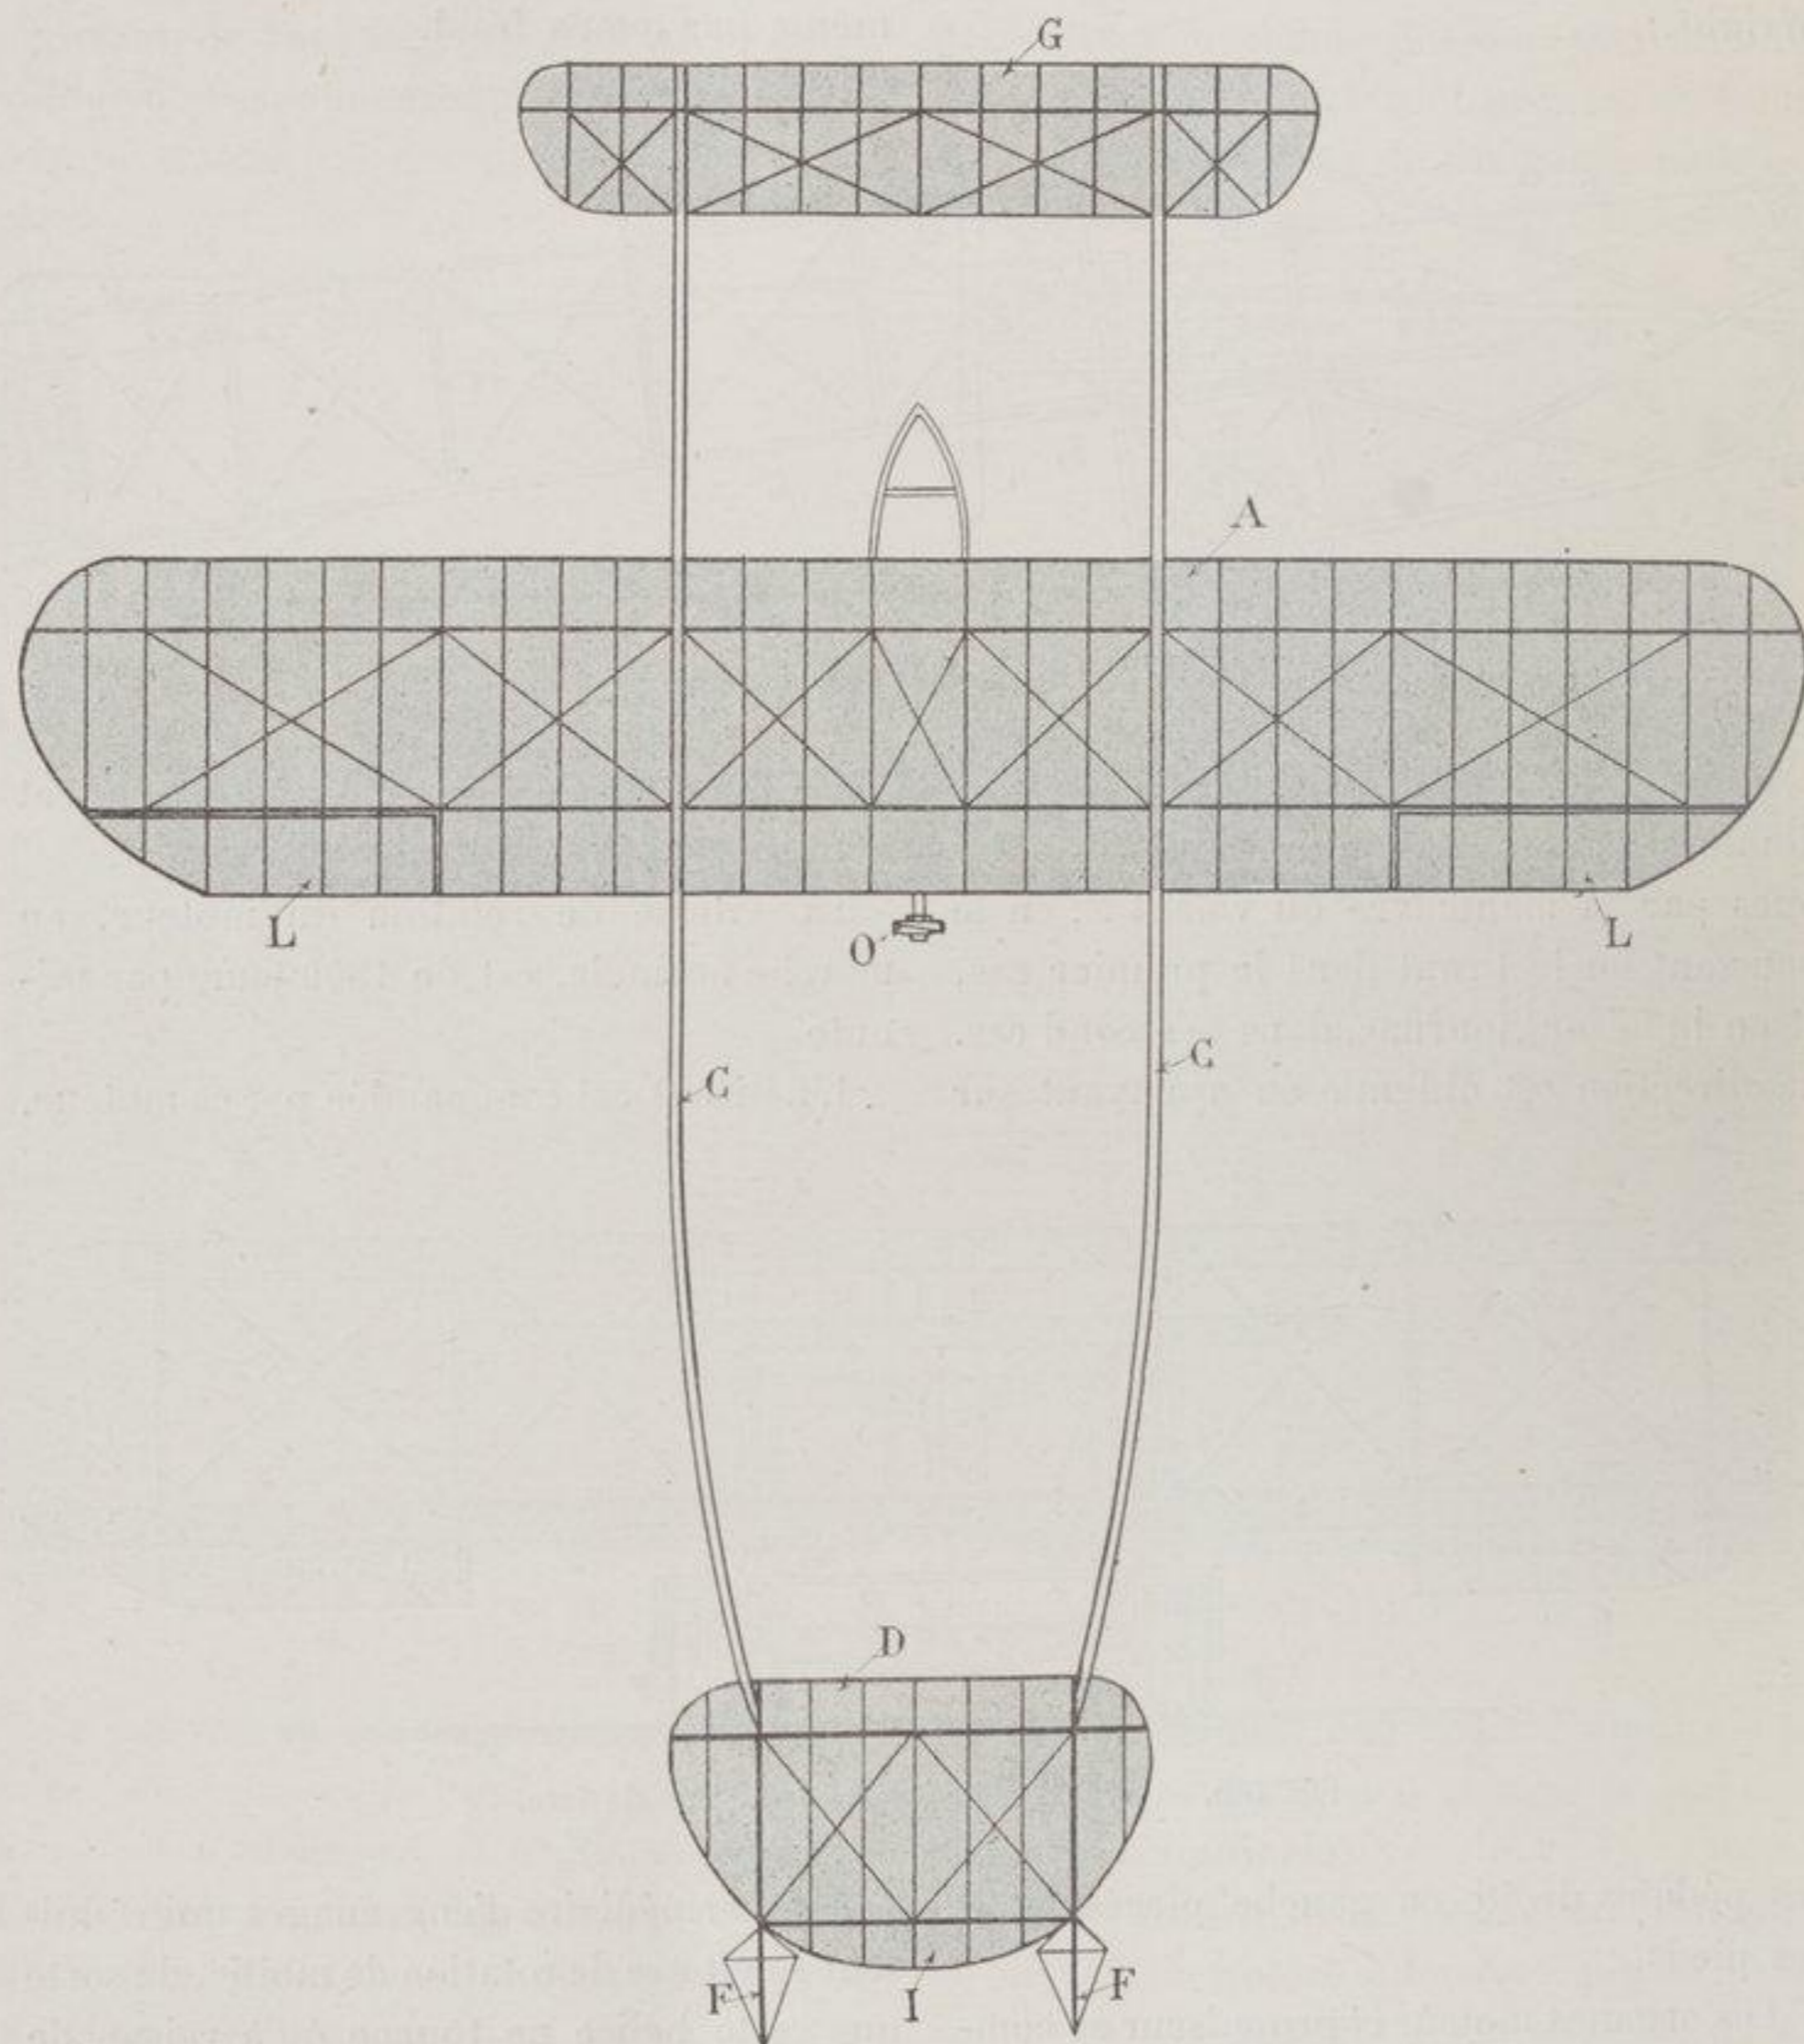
Biplan Maurice Farman. Vue en plan.
